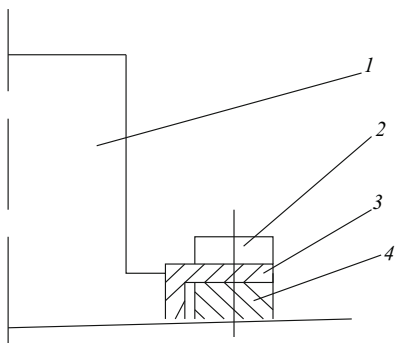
Фиксация гайки поршня РК по сборочному чертежу рабочего колеса ГА-1:
